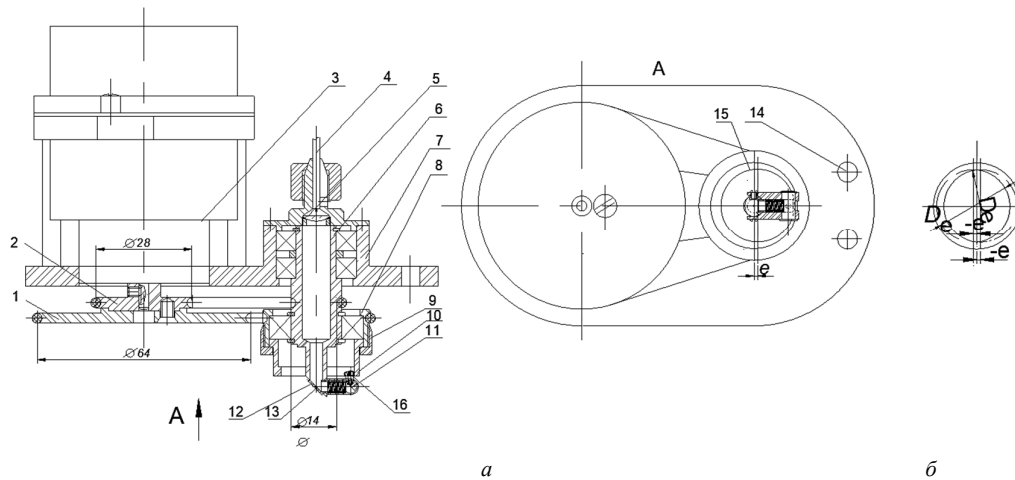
Конструкція сканера фізіотерапевтичної установки (а: 1, 2 – шків на валу електродвигуна 3; 4 – світло волокно від лазера; 5 – лінза коліматор; 6 – втулка-вал; 7 – корпус; 8 – шків-втулка дзеркала; 9 – гайка кулачка 15; 10 – повідець; 11 – циліндрична вісь повідця; 12 – дзеркало поворотне; 13 – отвір; 14 – отвори монтажні; 15 – кулачок; 16 – отвір-профіль кулачка, б – профіль кулачка 15)
